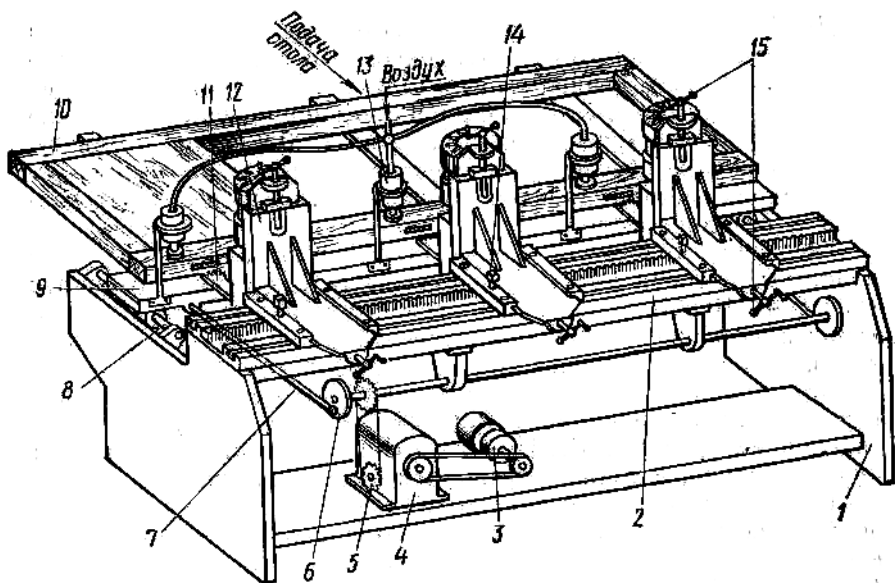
Долбежный станок для выборки гнезд под петли в полотнах дверей:
